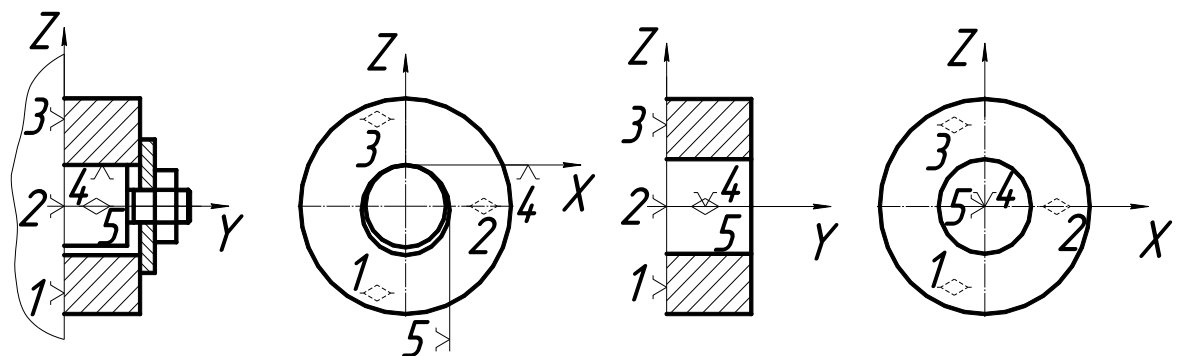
Базування за короткою внутрішньою поверхнею обертання:
